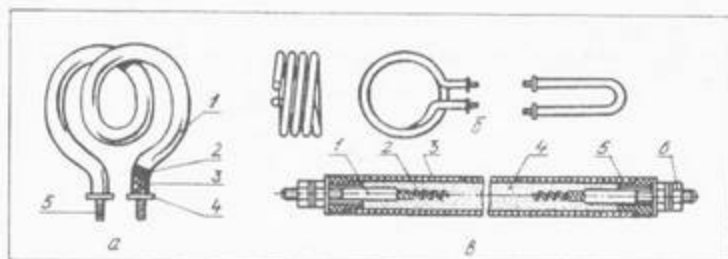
Электронагреватель закрытый: а — трубчатый: 1 — металлическая трубка, 2 — спираль, 3 — кварцевый песок, 4 — контактная шпилька, 5 — стекловидная эмаль; б — виды трубчатых электронагревателей; в — устройство одного из них: 1 — контактный стержень, 2 — нагревательный элемент, 3 — оболочка, 4 — наполнитель, 5 — герметическая пробка, 6 — контактная гайка
